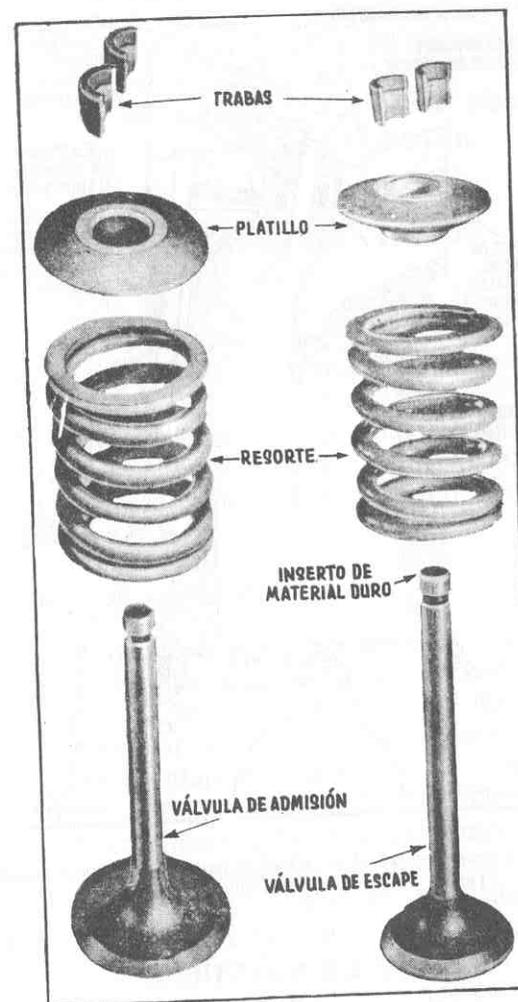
Conjunto de válvulas del motor 221 SP.
